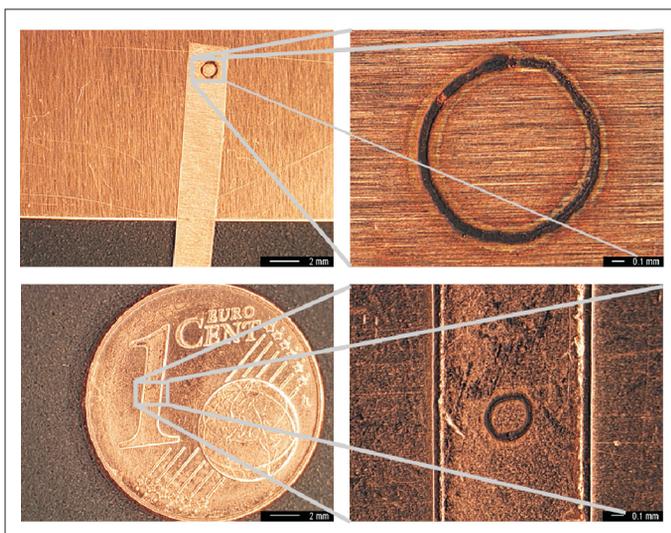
oben: $50\mu\text{m}$ dicke Kupferfolie auf Grundkörper geschweißt. unten: Einschweißung auf einem 1-Cent-Stück zum Größenvergleich.
